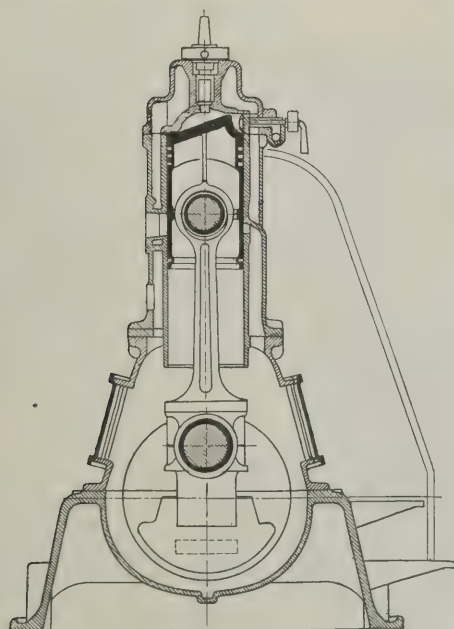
Querschnitte durch einen Zylinder des Ellwe-Motors. M. rd. 1:30.
